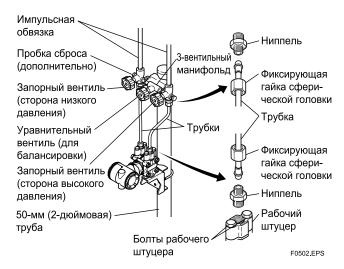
3-вентильный манифольд (монтаж на трубе)
